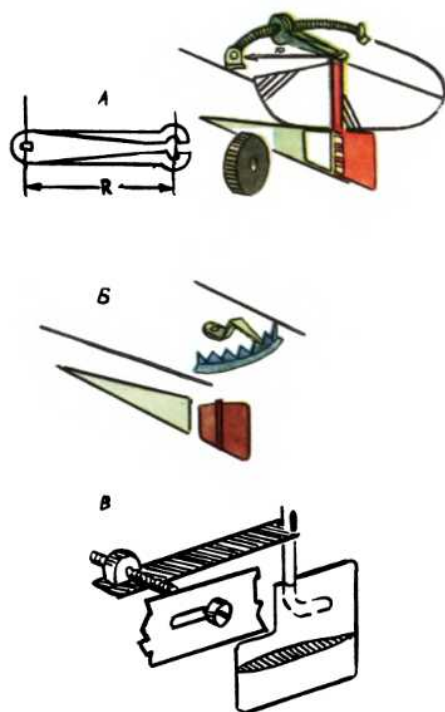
Различные приспособления для регулировки и фиксации руля: А — с поворотной гайкой; Б — с гребенкой; В — с регулировочным винтом.
